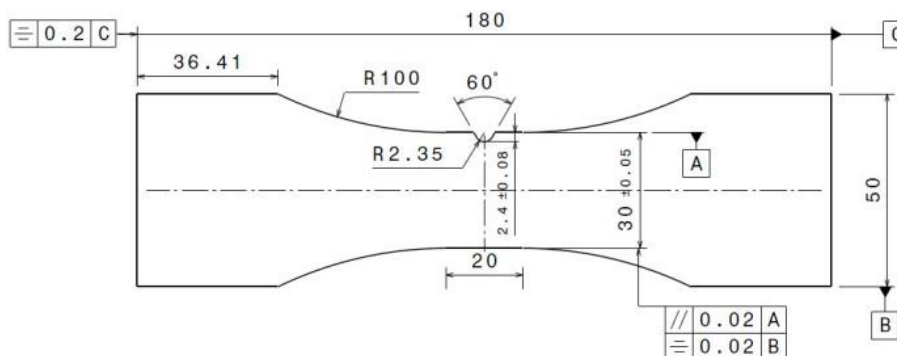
Géométrie de l'éprouvette de fatigue entaillée $K_t=3$
